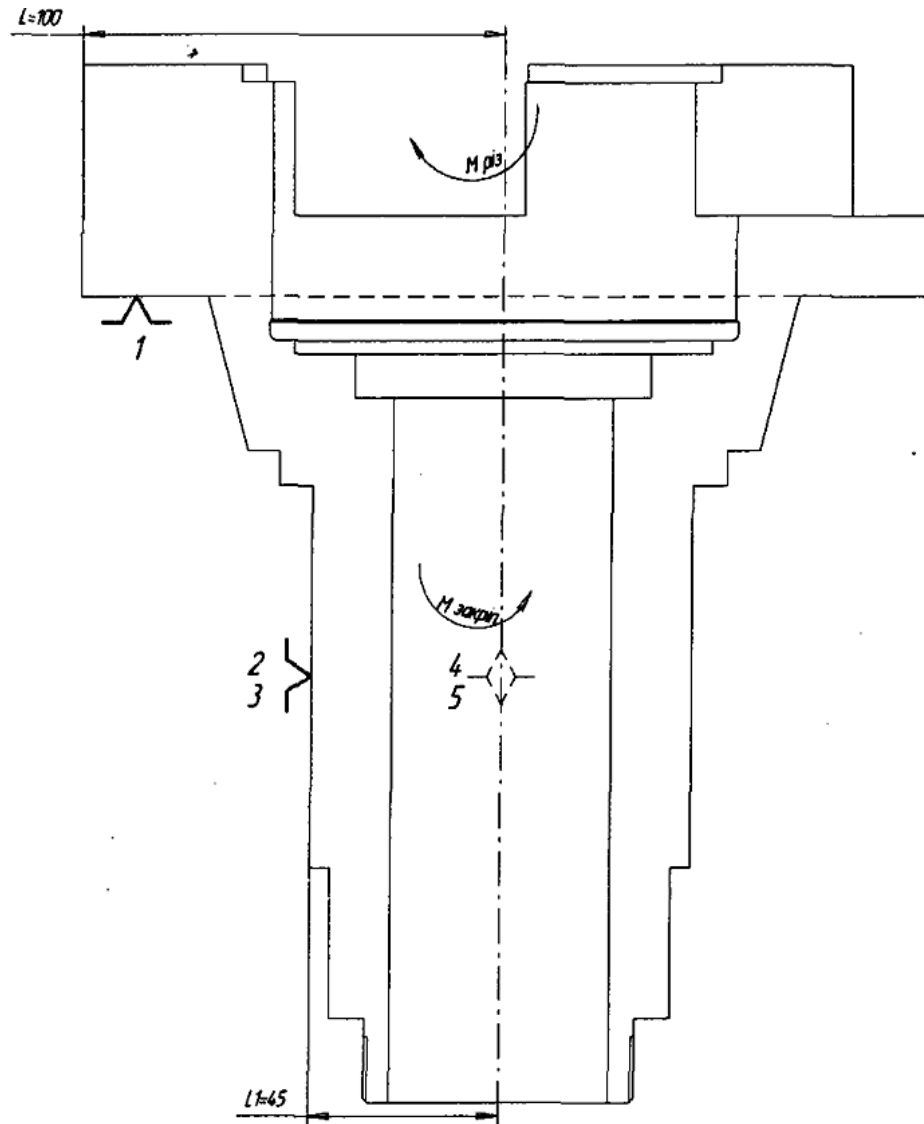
Схема базування корпусу шліцевого у пристрої
